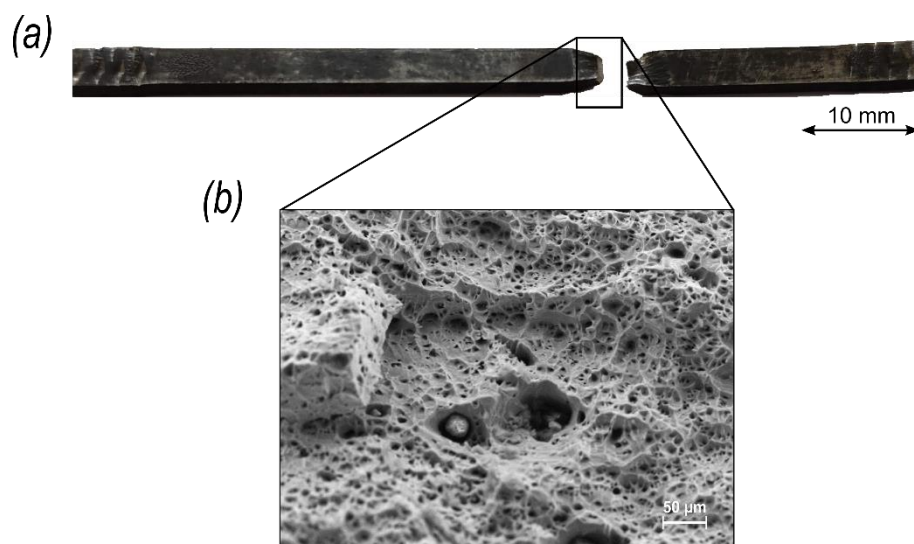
(a) #6_LAE_2_800°C_1H após ensaio de tração uniaxial. (b) Superfície de fratura.
